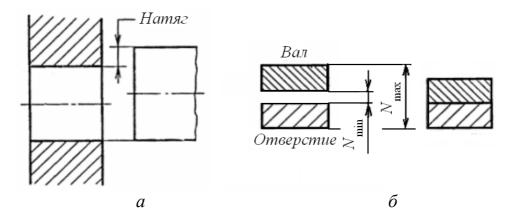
Посадка с натягом: a — общий вид; δ — схема расположения интервалов допусков
